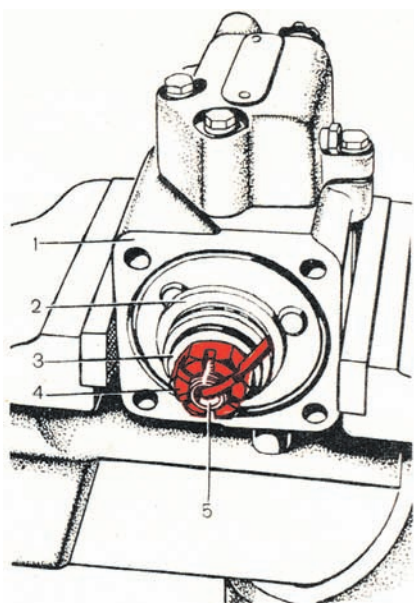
Разборка распределителя и снятие червяка. 1 — корпус; 2 — подшипник; 3 — шайба; 4 — сферическая гайка; 5 — червяк.
